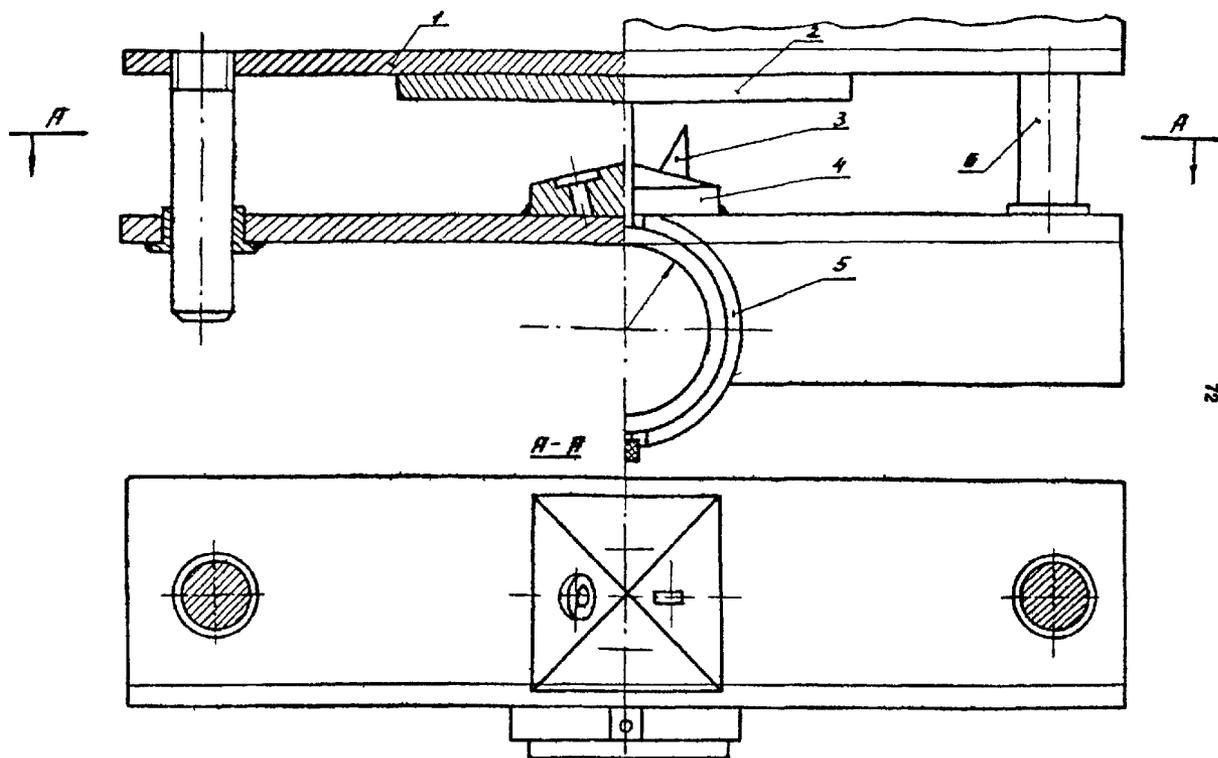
Устройство для нанесения зарубки способом вдавливания: 1 - уголок ; 2 - образец ; 3 - боек ; 4 - патрон ; 5 - оправка индикатора ; 6 - направляющая.
